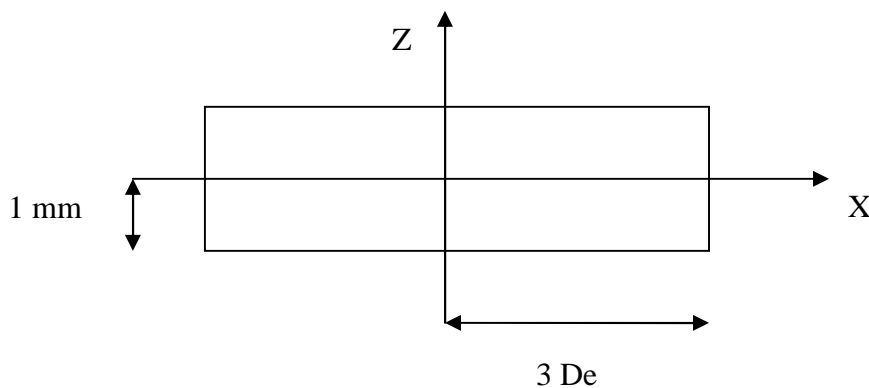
Dimension de la plaque à soudé.
